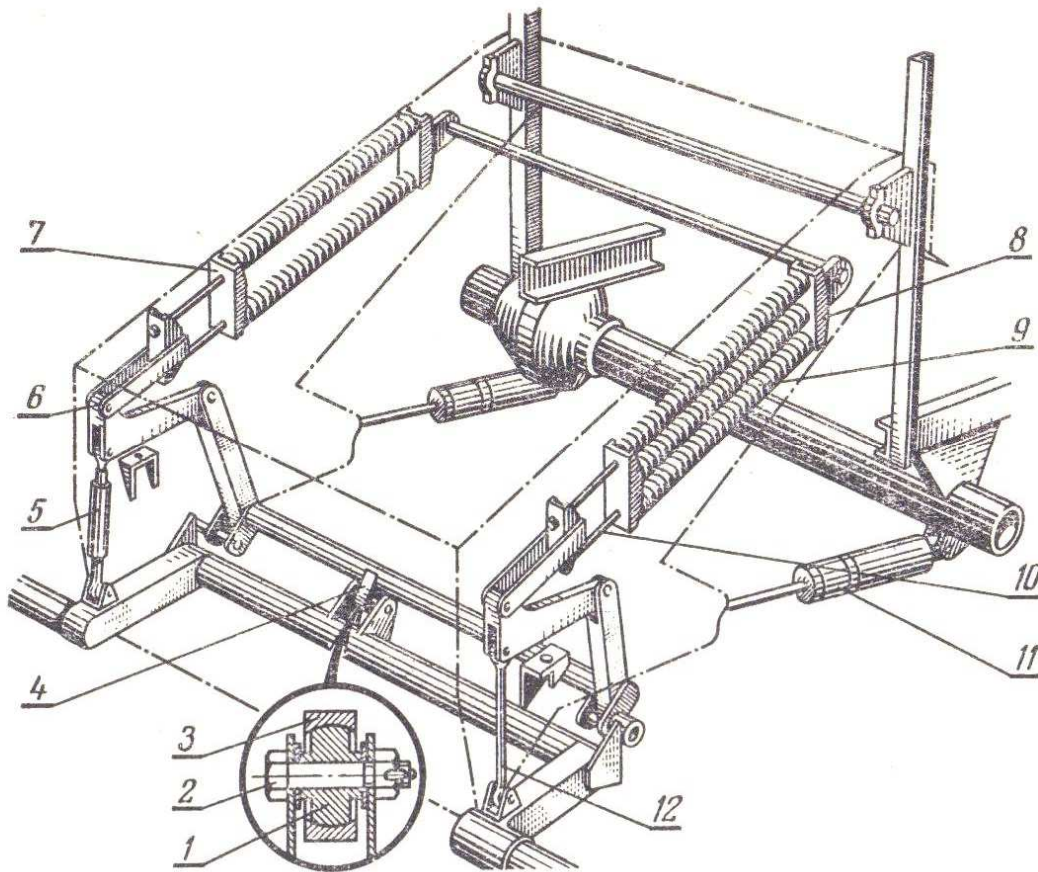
Схема подвески и уравновешивания корпуса жатки комбайна СК-6: 1 – сферическое кольцо; 2 – болт; 3 – кронштейн; 4 – центральный сферический шарнир; 5, 12 – подвески; 6 – рычаг; 7, 8 – блоки пружин; 9 – пружины; 10 – регулировочный болт; 11 – гидроцилиндр
